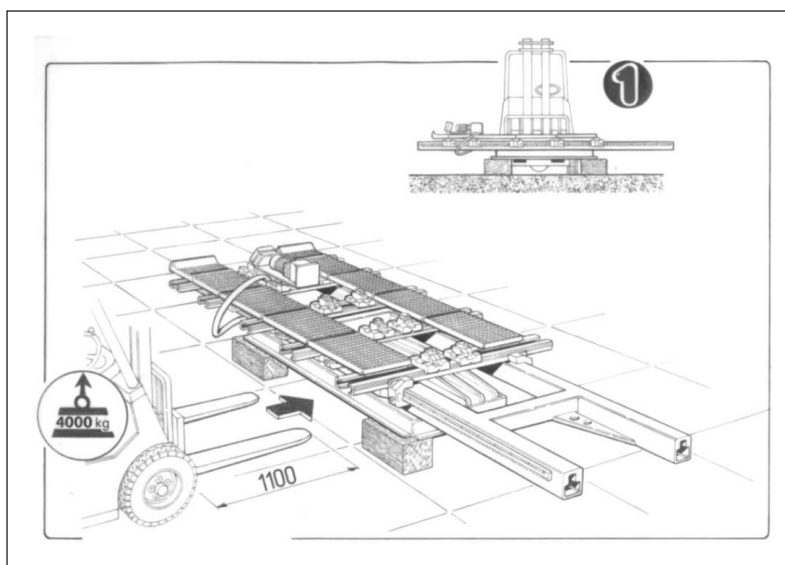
ESQUEMA DE LA INTRODUCCION LATERAL DE LA HORQUILLA EN LA BANCADA
